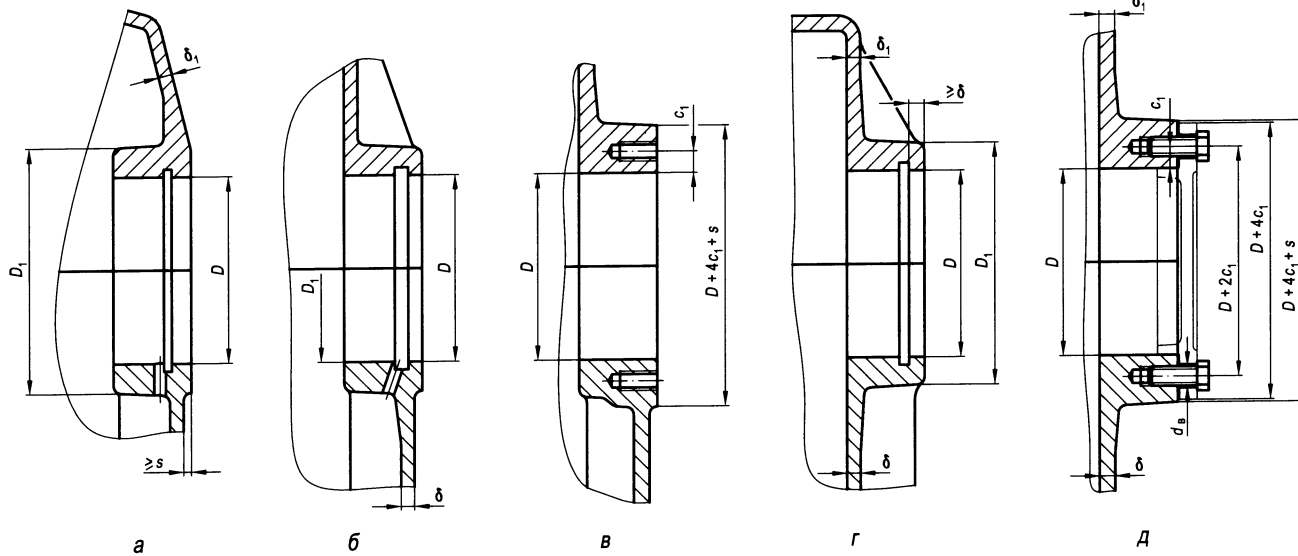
Приливы (обышки) для подшипников (размеры см. в табл. 23.2.1)
